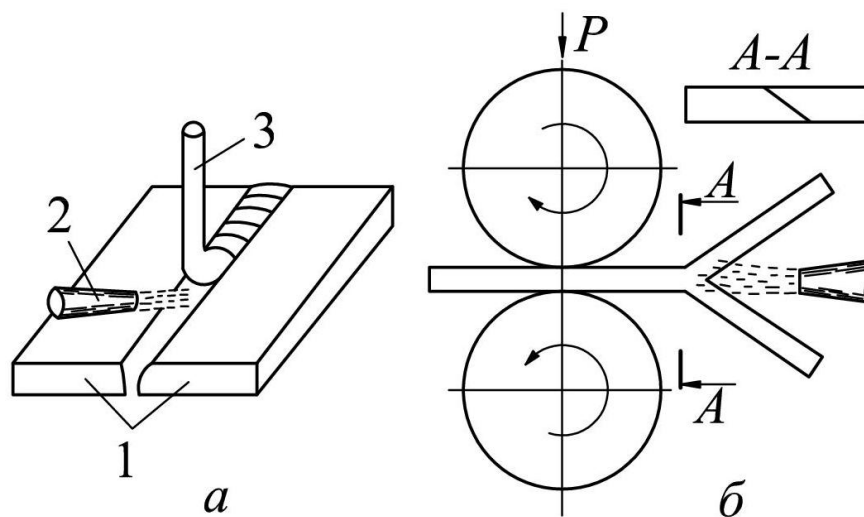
Схема зварювання газовим теплоносієм з присадочним (а) і без присадочного (б) матеріалів
